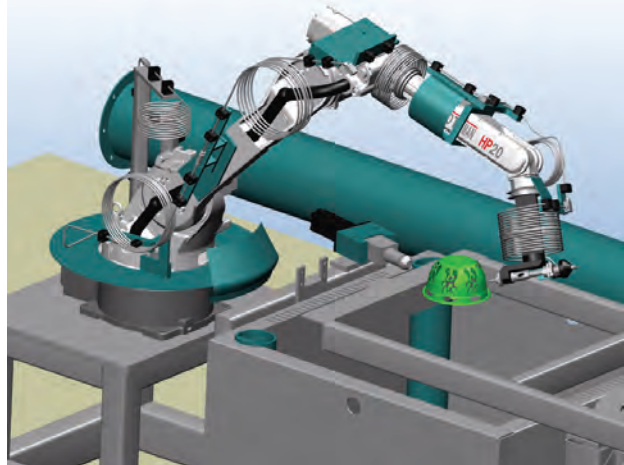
Paralelní zpracování tří úloh najednou (Multi-threading)
